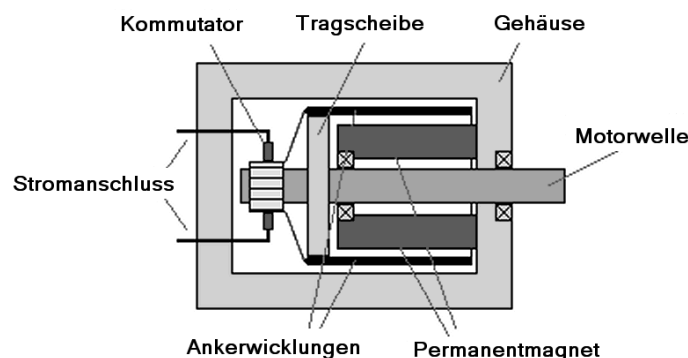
Prinzipieller Aufbau eines Glockenankermotors
